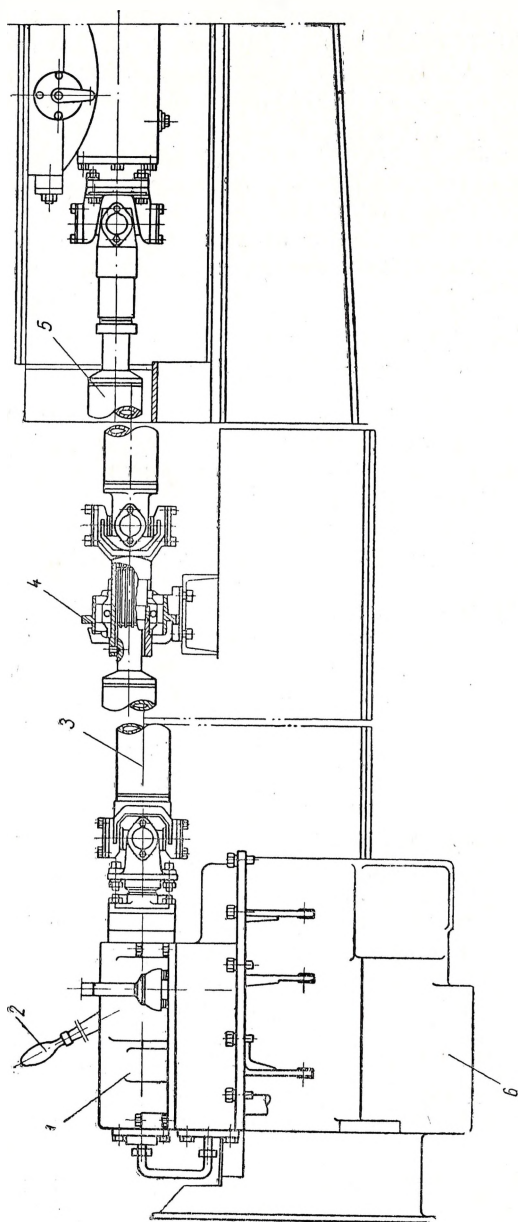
Схема устройства дополнительной силовой передачи автоматической лестницы АМ-45:
